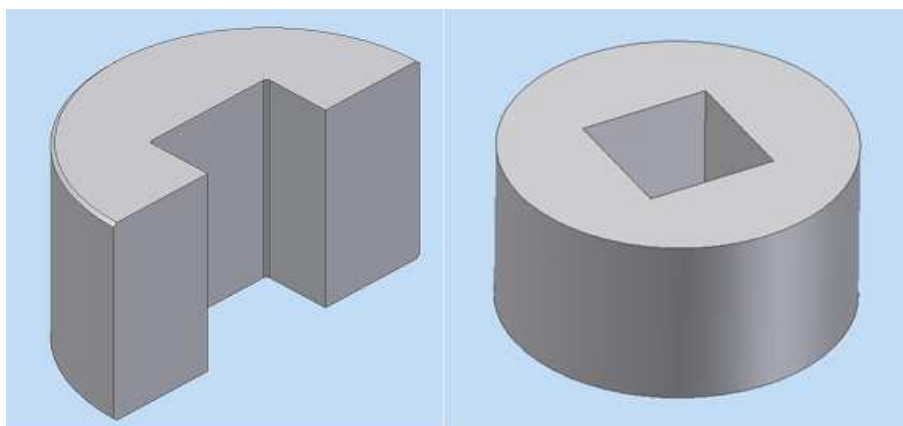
Comparação entre duas versões para o corpo do molde. A versão do lado direito é mais difícil de maquinar, o que implicaria aumento dos custos de produção do molde.
